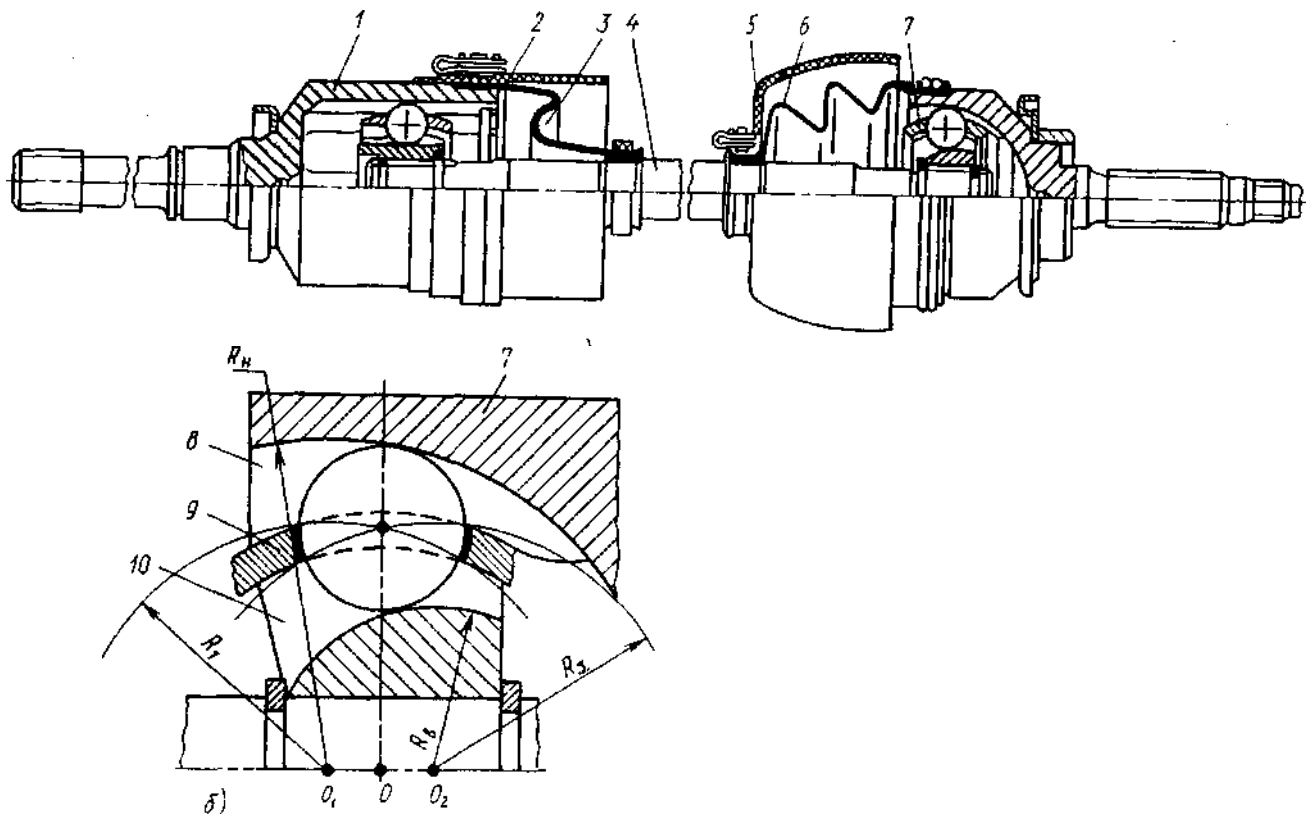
Привод переднего колеса автомобиля ВАЗ-2121 «Нива»: а - конструкция; б - схема наружного шарнира
